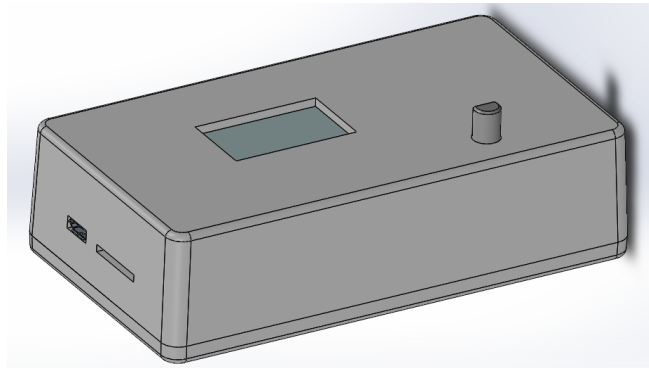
Vista del ensamblaje final en SolidWorks
